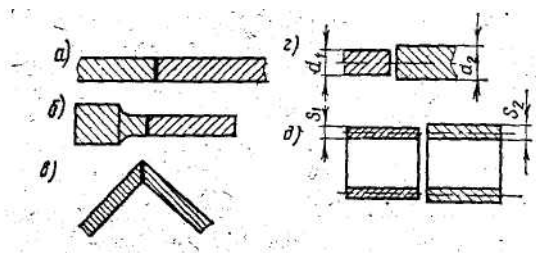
З'єднання при стиковому контактному зварюванні
